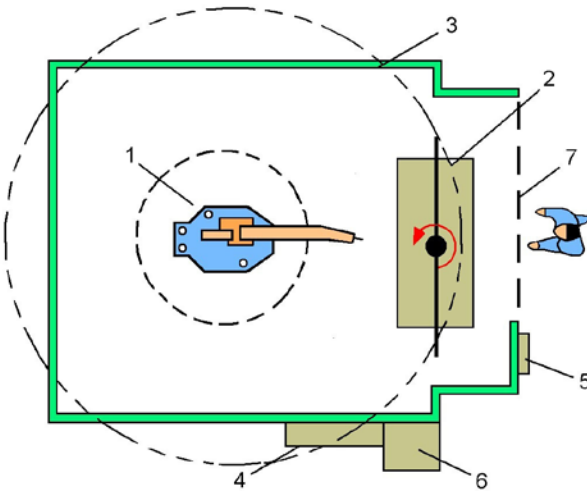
Schweißzelle mit zeitlich paralleler Beschickung der Schweißvorrichtung.
